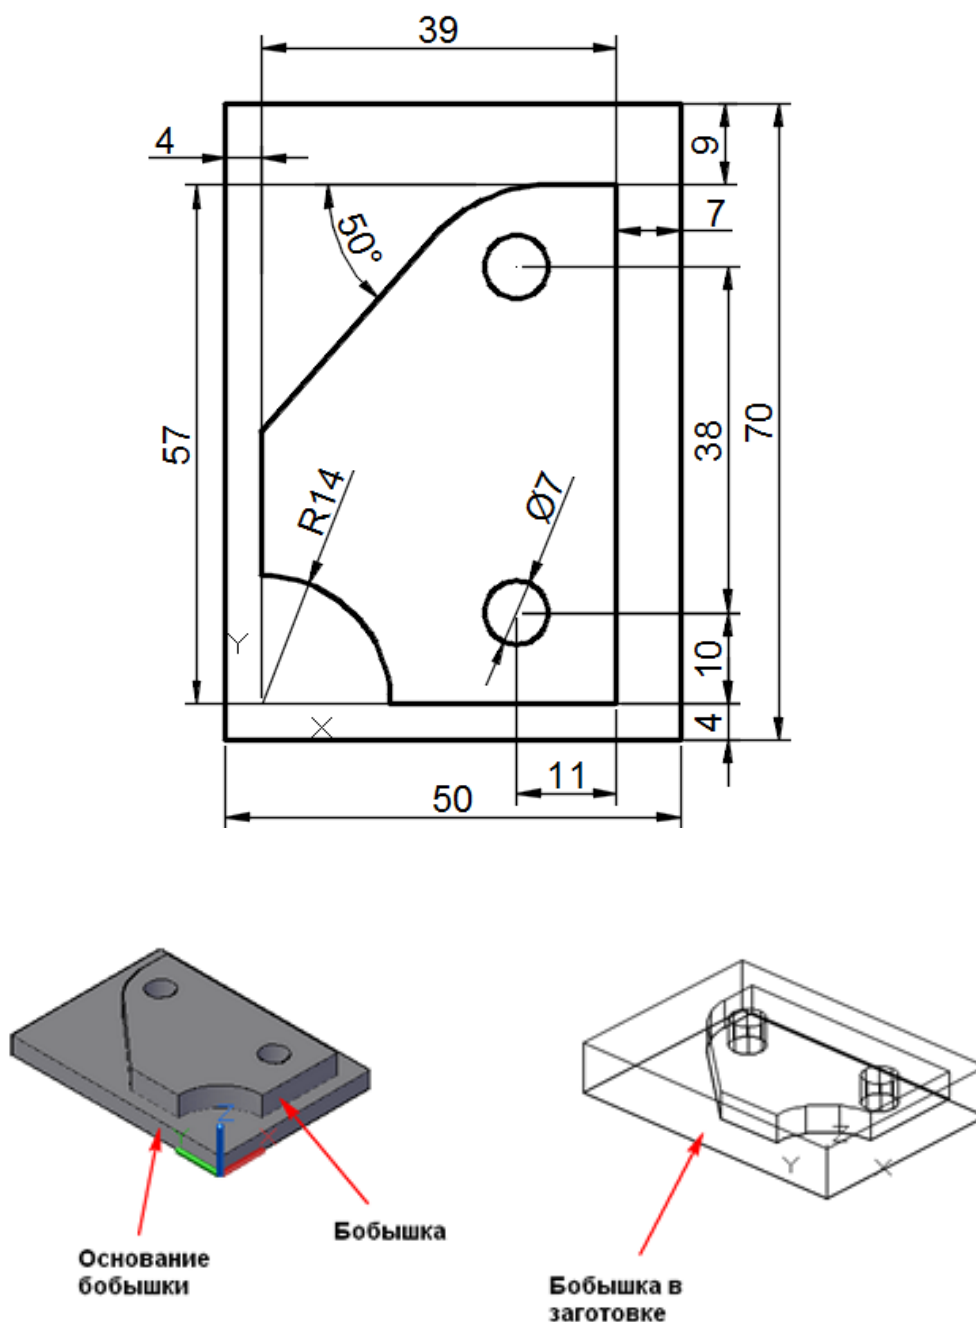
Эскиз и 3D-модель бобышки (Контур.dwg) [5]
